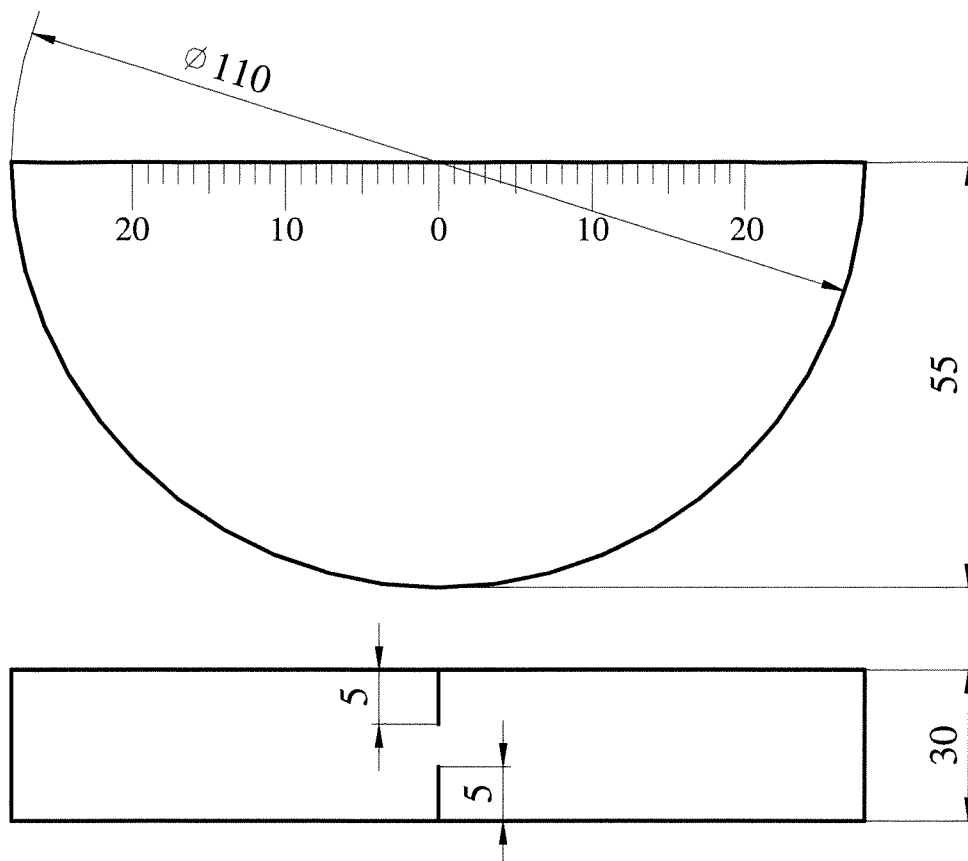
Стандартный образец СО-3 (материал – Ст3)
